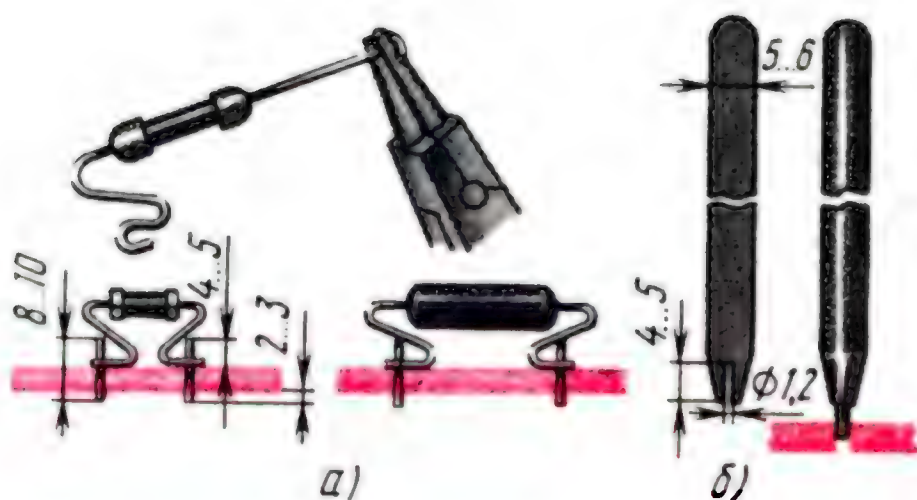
Монтаж деталей на шпильках (проволочных стойках) и приспособление для запрессовки шпилек
